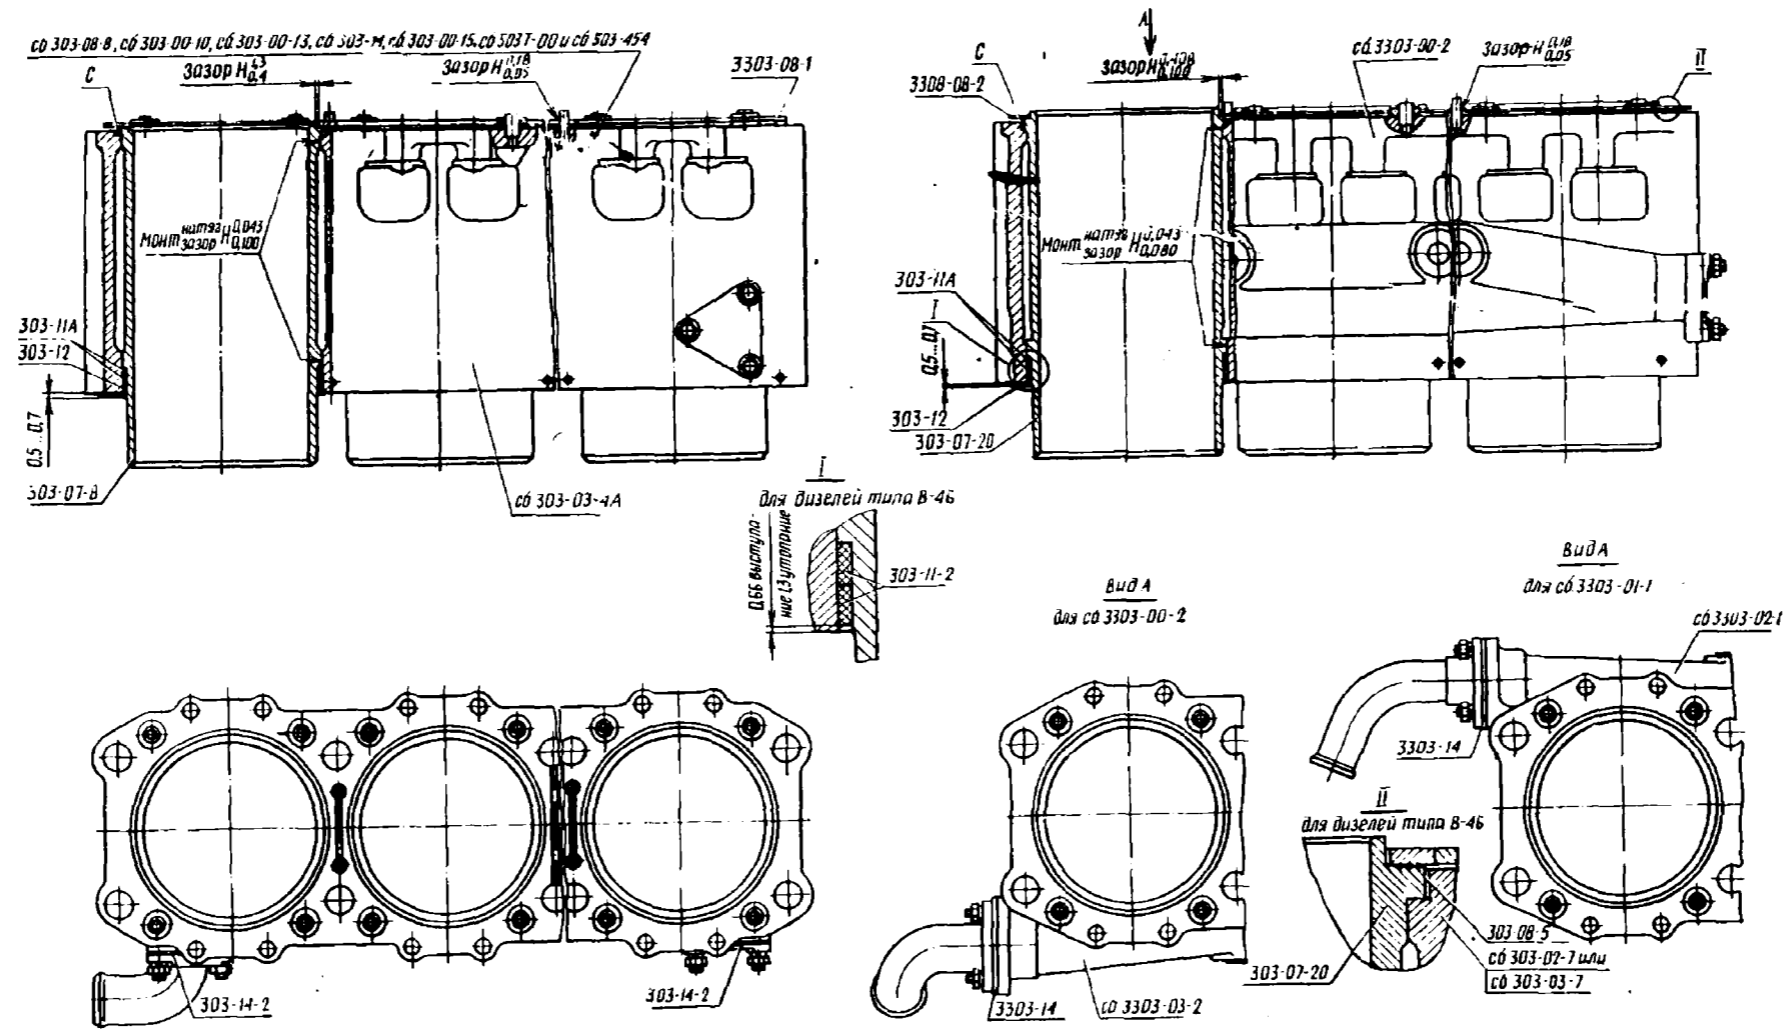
Блок цилиндров для дизелей типа В-2, типа В-46 и типа В-6:
